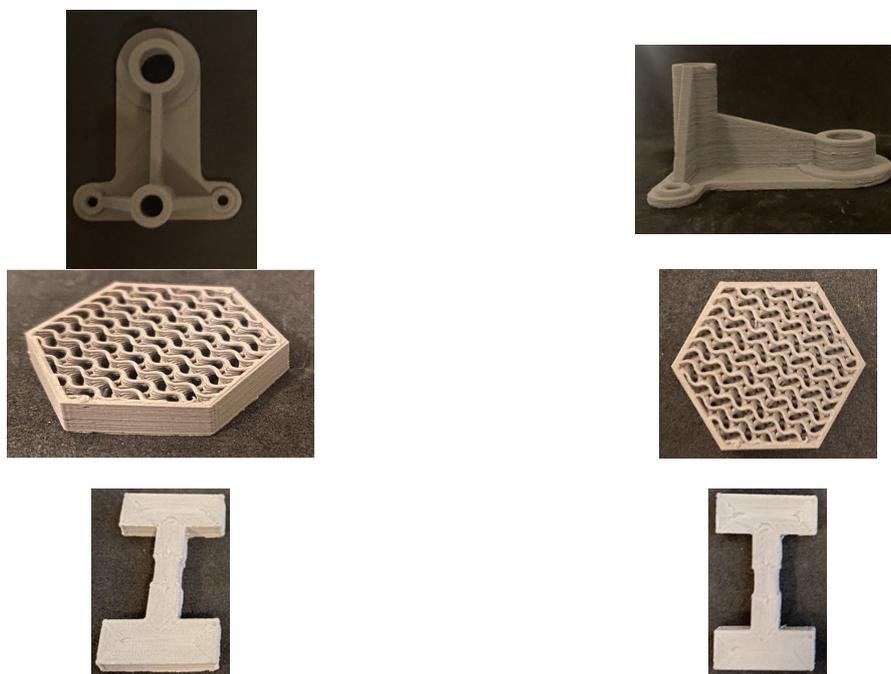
Pièces imprimées en 3D (pièces vertes).
